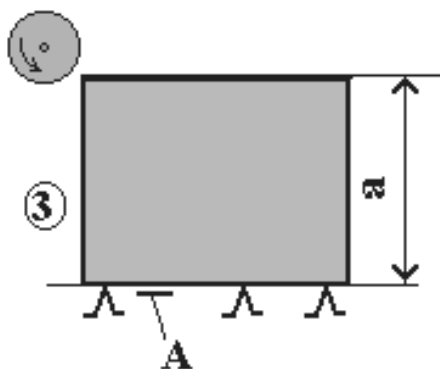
Пример *неполной схемы базирования* призматической заготовки.
